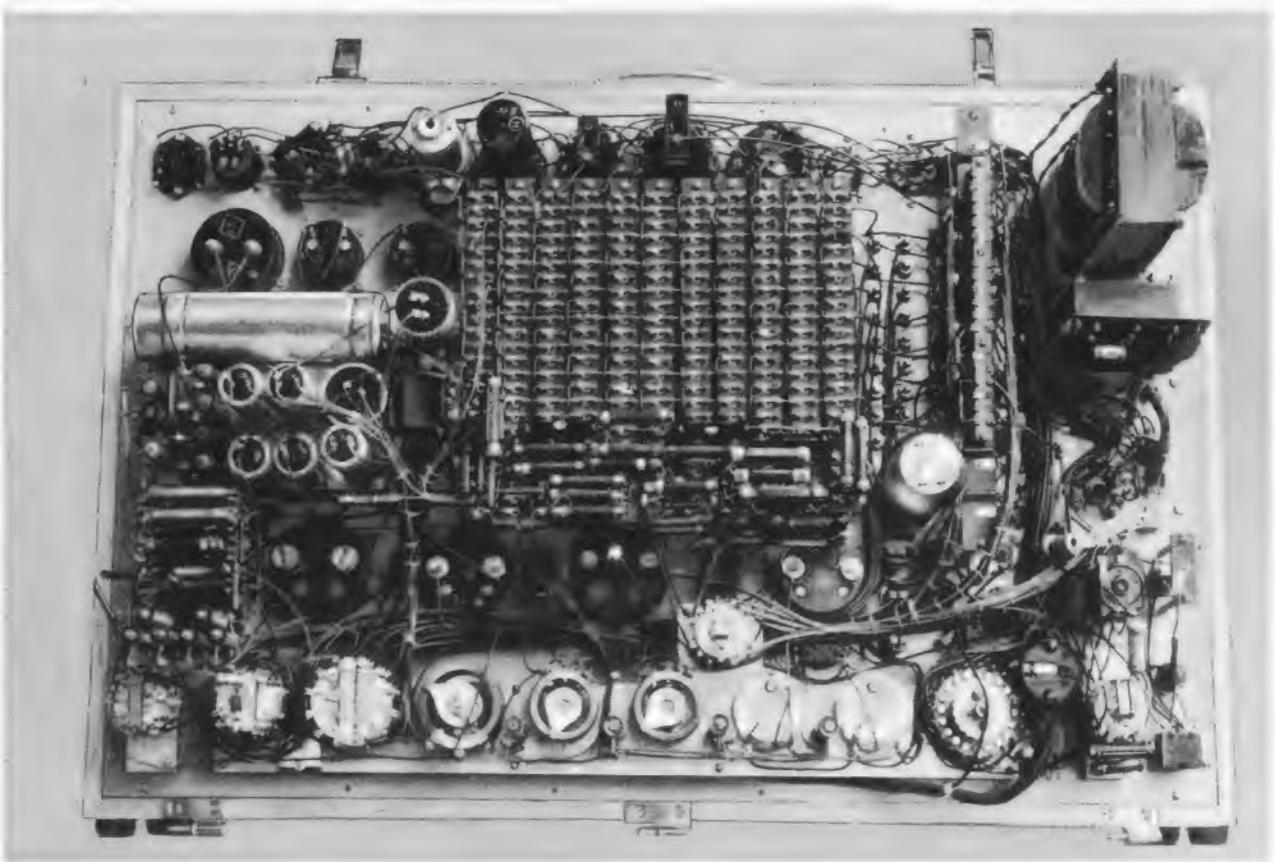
Innenansicht des fertig verdrahteten Röhrenmeßgerätes
